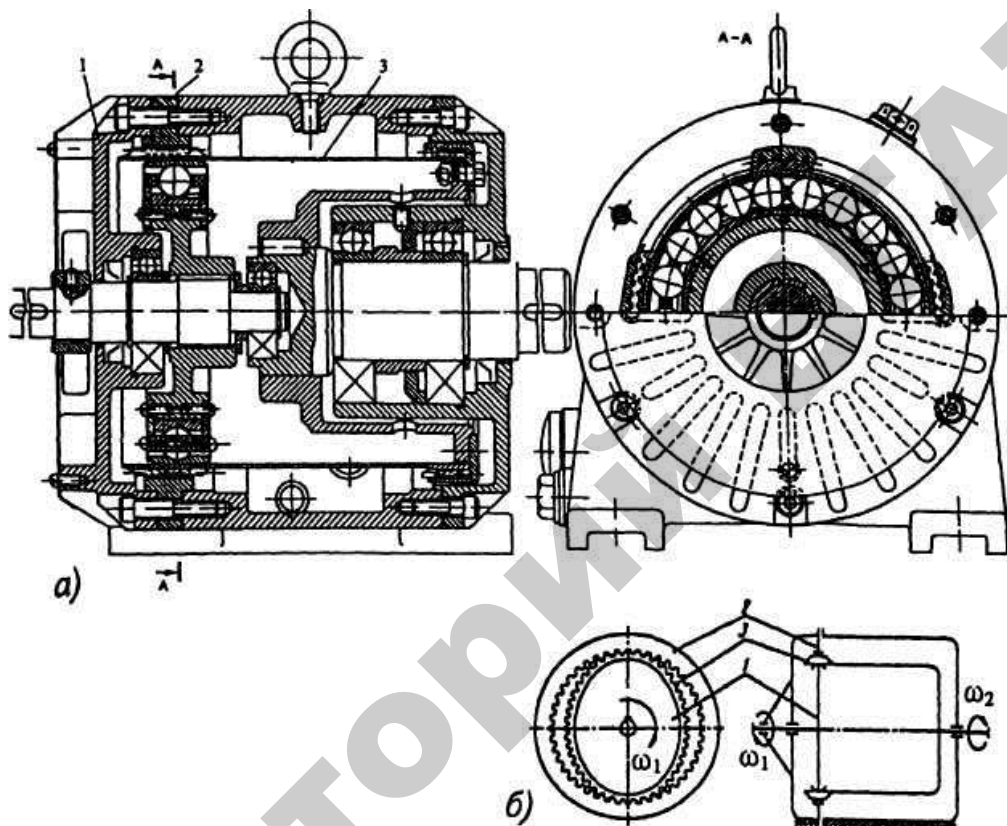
Волновой зубчатый редуктор: *a* — конструкция; *б* — кинематическая схема; 1 — генератор волн; 2 — жесткое колесо с внутренними зубьями; 3 — гибкое колесо
